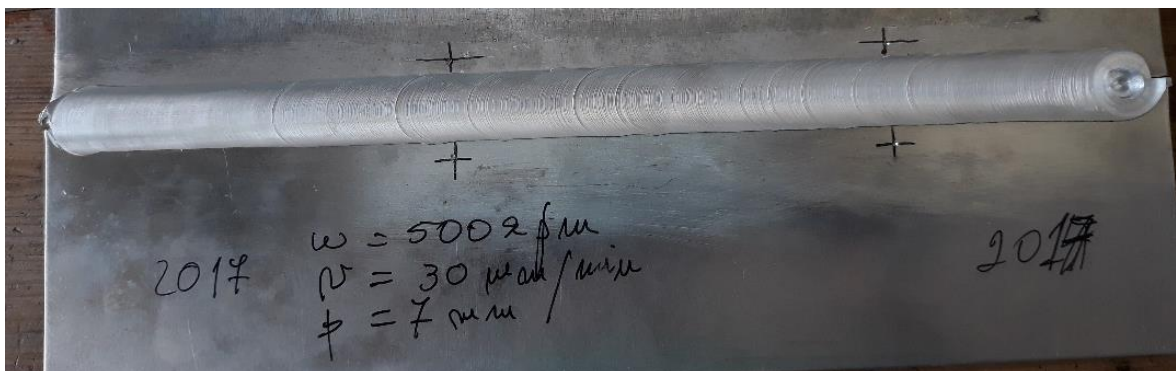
Estado superficial da soldadura 562BRP-1
